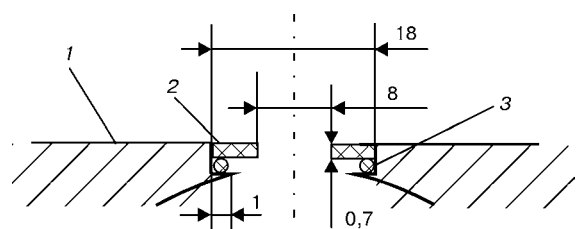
Схематическое изображение накладной пластины предметного столика с ограничительным и уплотняющим кольцами в поперечном разрезе: 1 — накладная пластина с отверстием; 2 — кольцо из нитрида бора; 3 — резиновое кольцо
